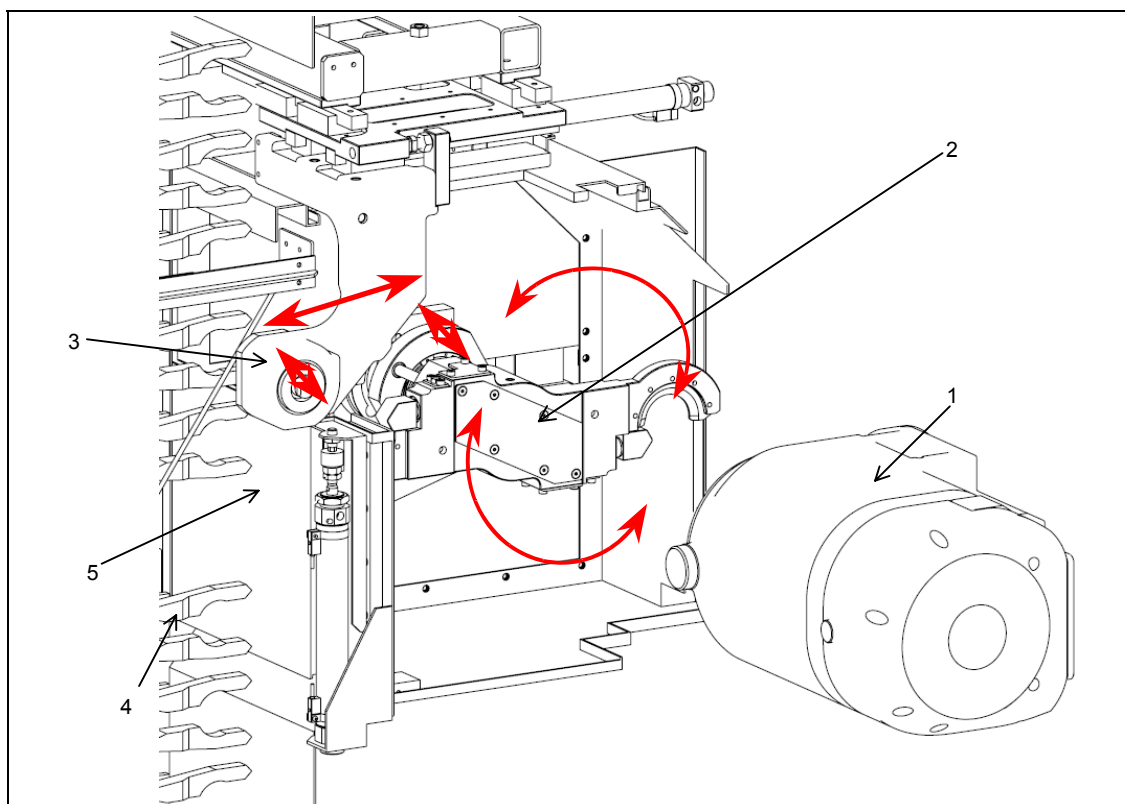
Устройство устройства АСИ (с магазином на 36 инструментов)
